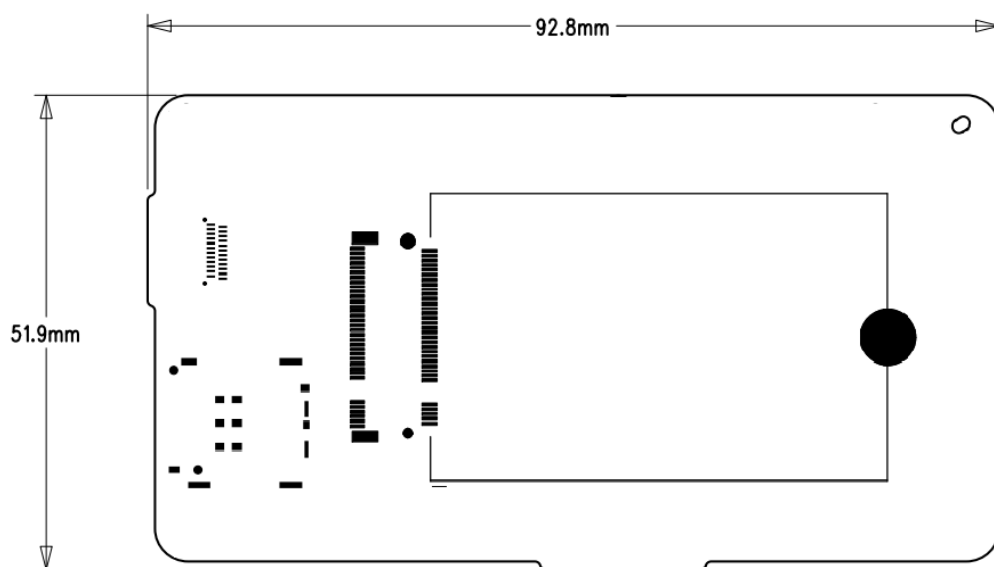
SMA5293 模组 PCB 布局和尺寸（单位：mm）
